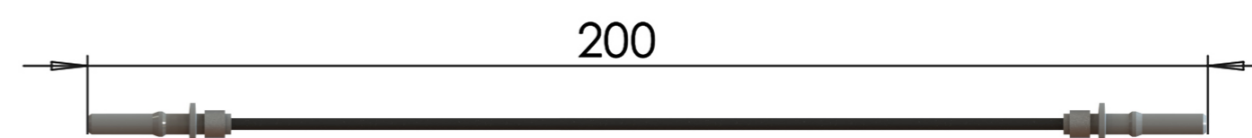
Внешний вид и габаритные размеры оптической перемычки
